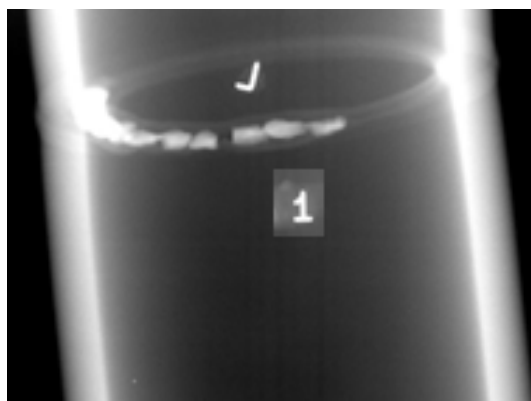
Рентгеновский снимок сварного стыкового шва полиэтиленовых труб $\varnothing 110 \times 10$ мм с цепочкой крупных твердых включений.
